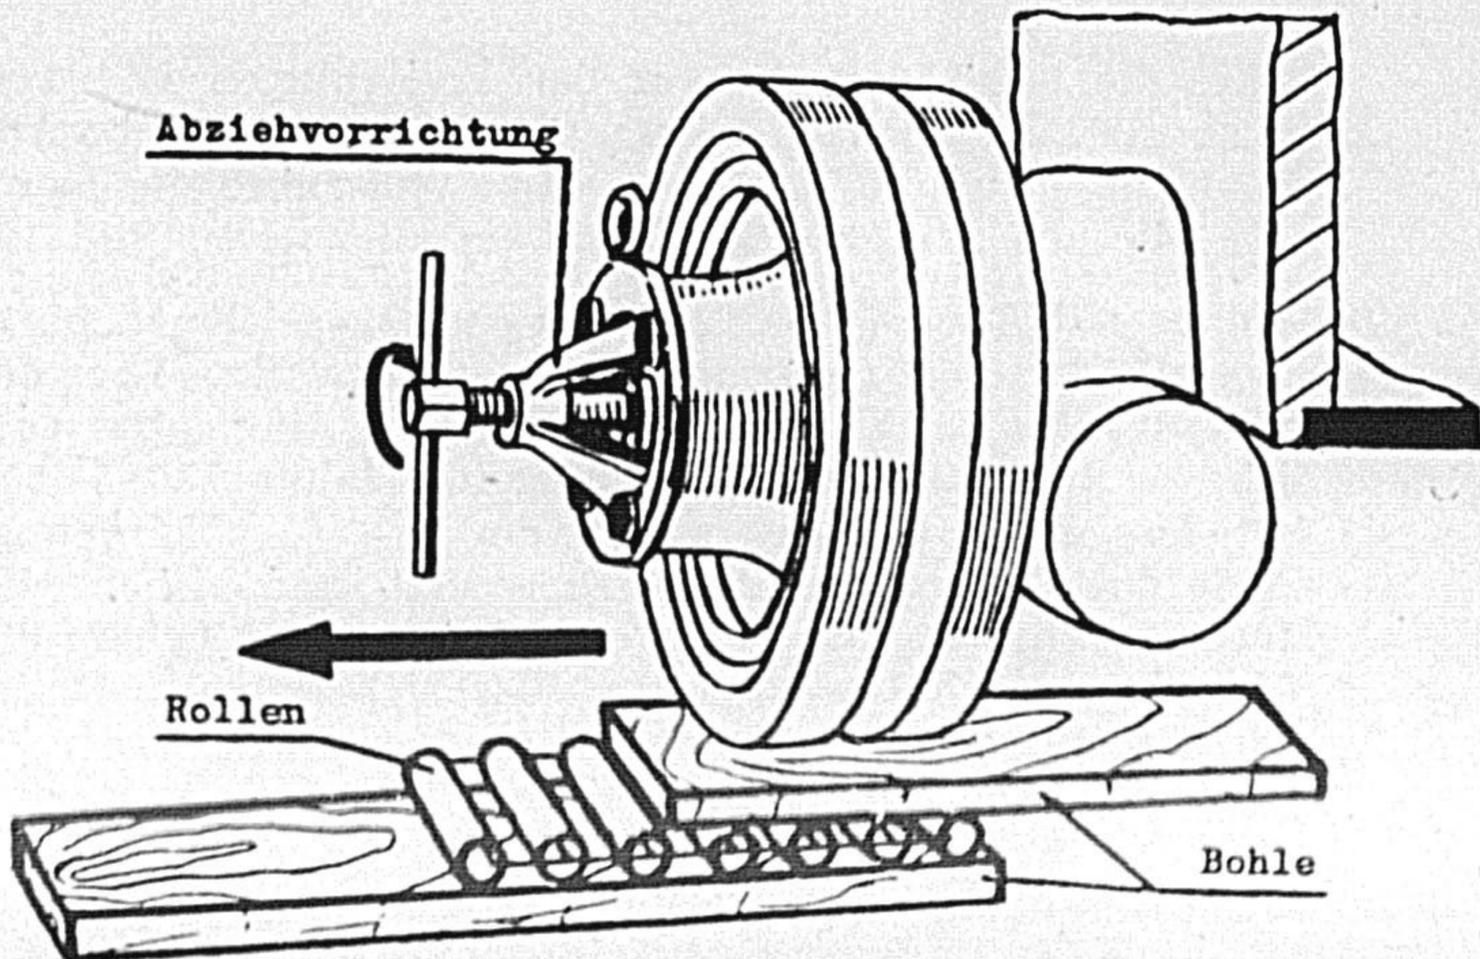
Ausbau der ersten Laufrolle mit Rollschlitten Sk 10.006
